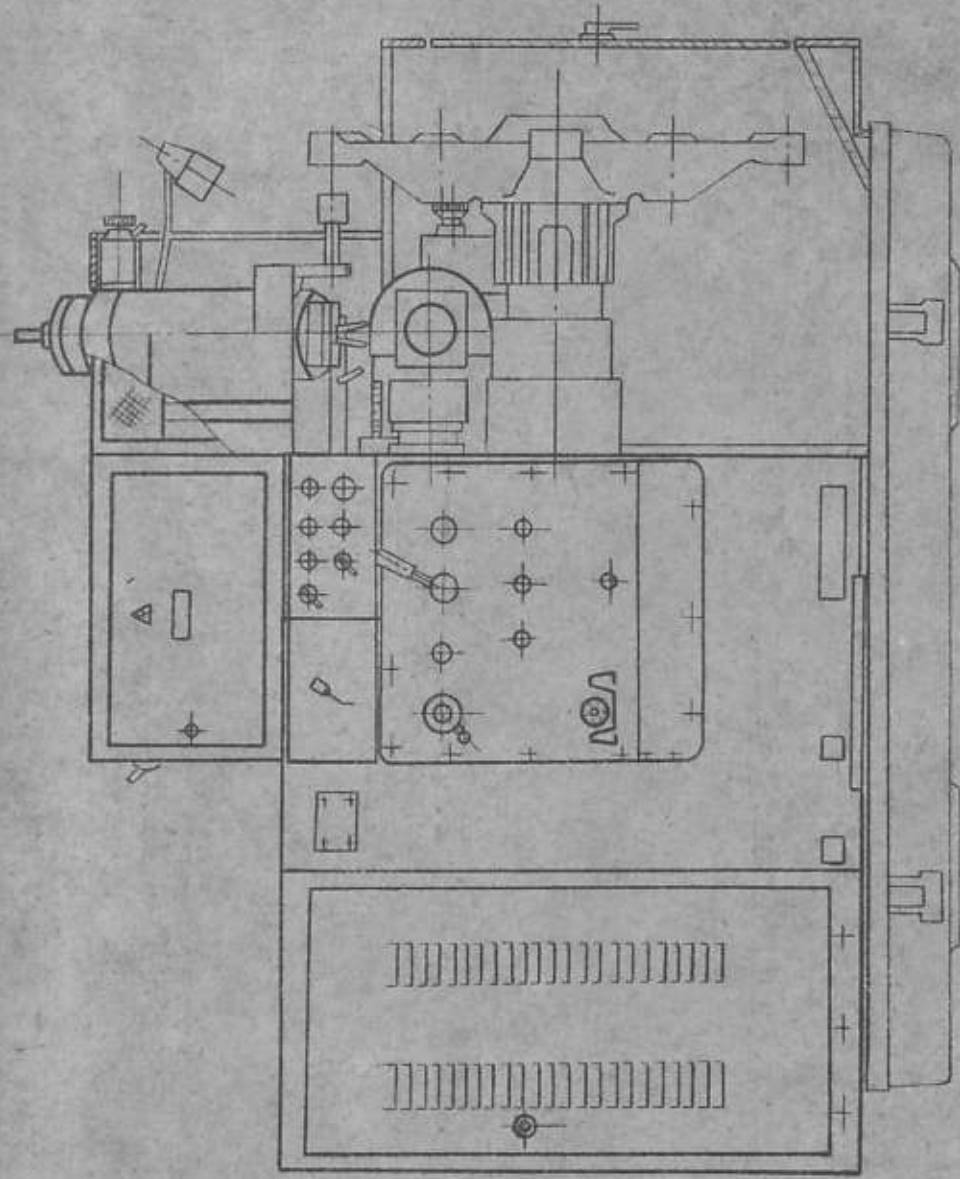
Токарно-револьверный полувальцоват мод 1Р416
